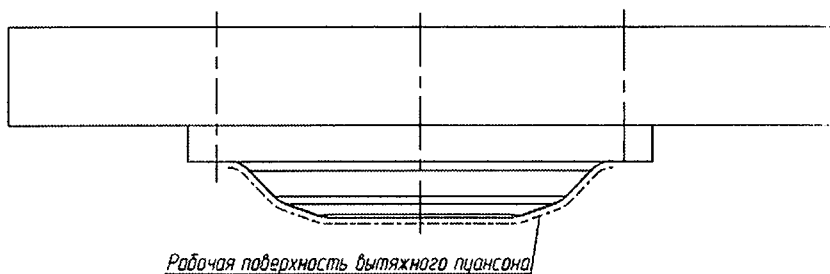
Пример крепления крупногабаритного пуансона непосредственно к верхней плите штампа
